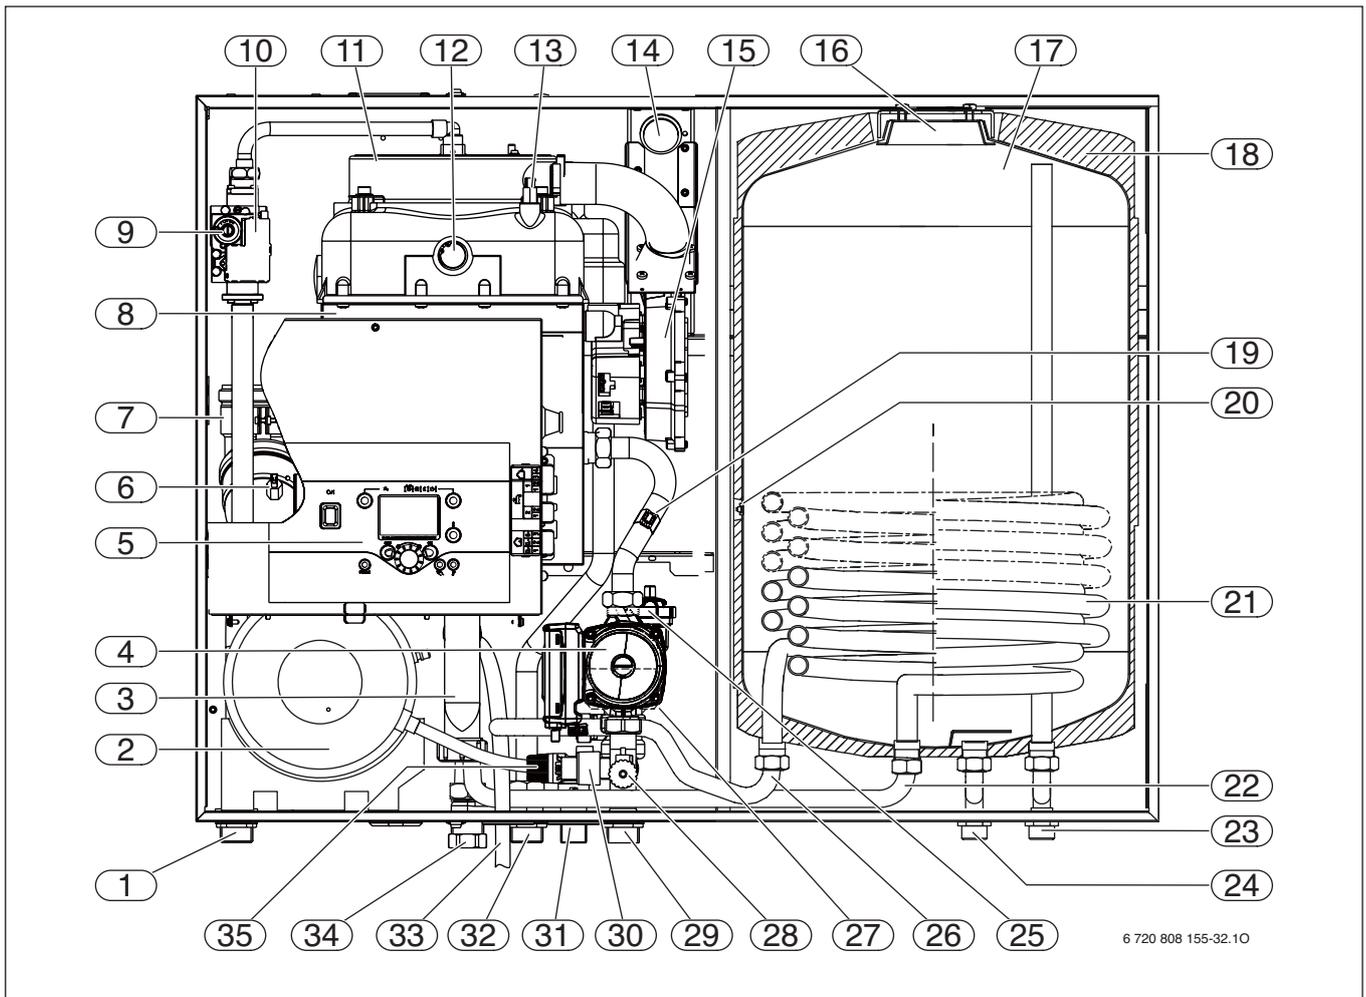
Layout caldaie THR 2-17/5-25 M75 H
